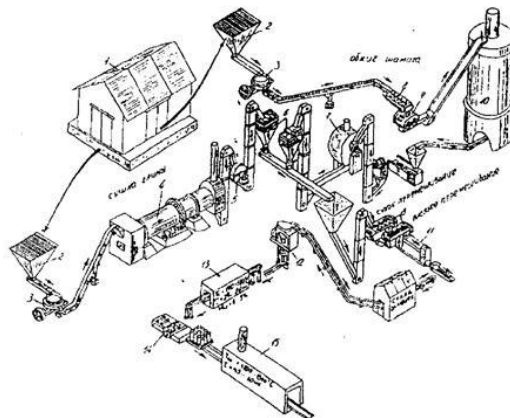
Технологічна схема виготовлення керамічних труб: 1 - склад глини; 2 - бункери для глини; 3 – стругачі; 4 - сушильний барабан; 5 – дезінтегратор; 6 – грохоти; 7 - кульовий млин; 8 – змішувачі; 9 - брикетні вальці; 10 - шахтна піч; 11 - вакуум-прес; 12 - трубний прес; 13 - сушарка.; 14 - глазурувальна машина; 15 - піч для випалювання.
